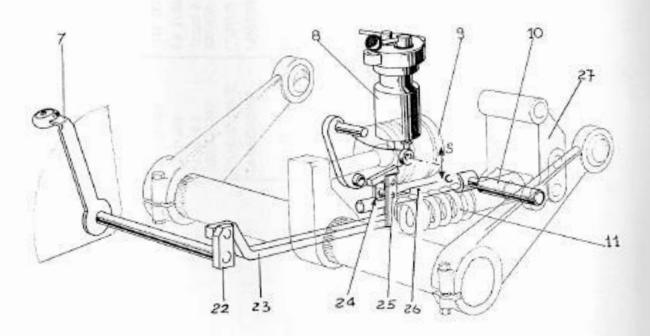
Vue d'ensemble du dispositif de relevage hydraulique
